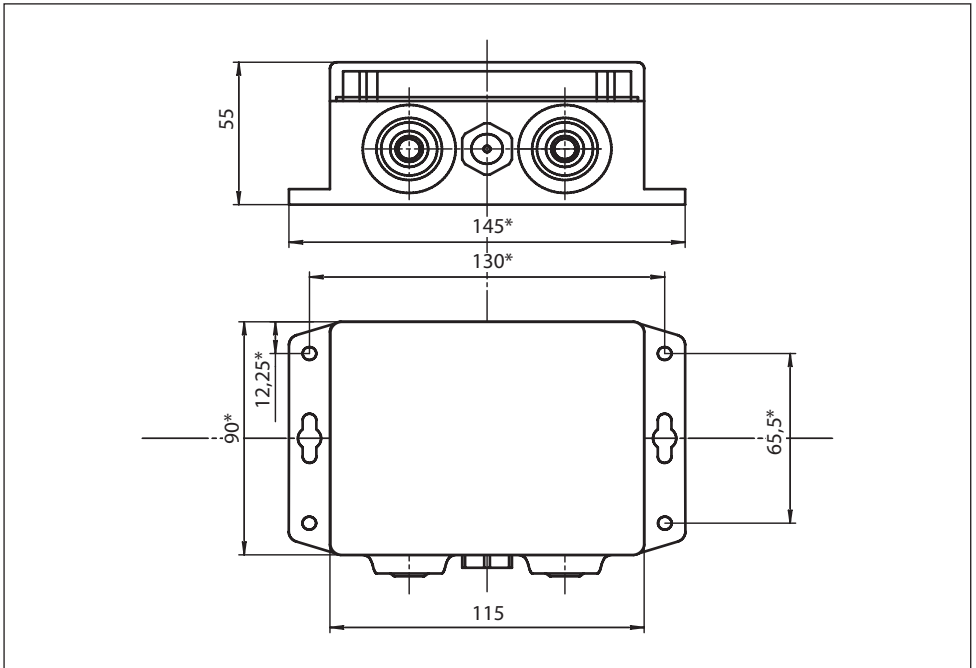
Габаритный чертёж контроллера "Сенсон К-1М"
